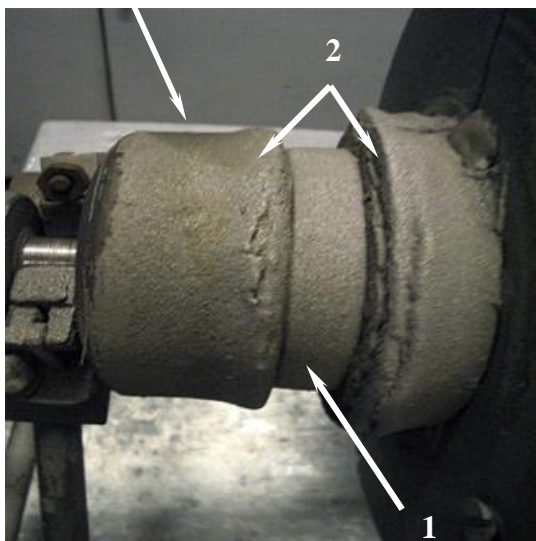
Барабан ротора компрессора с приспособлениями:
